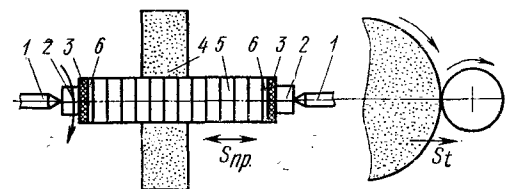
Кругление заготовок на круглошлифовальном станке
